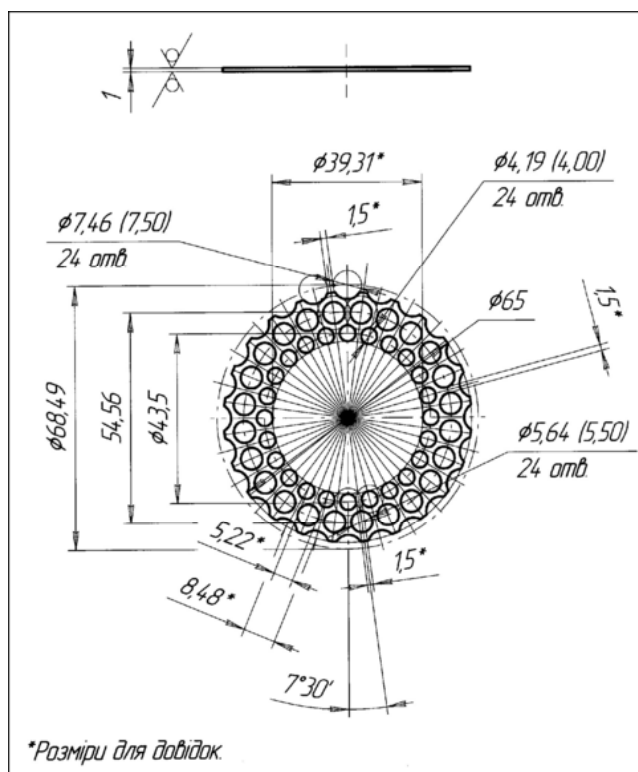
Креслення розрахункової вихідної заготовки для витягування за новим способом, що пропонується
